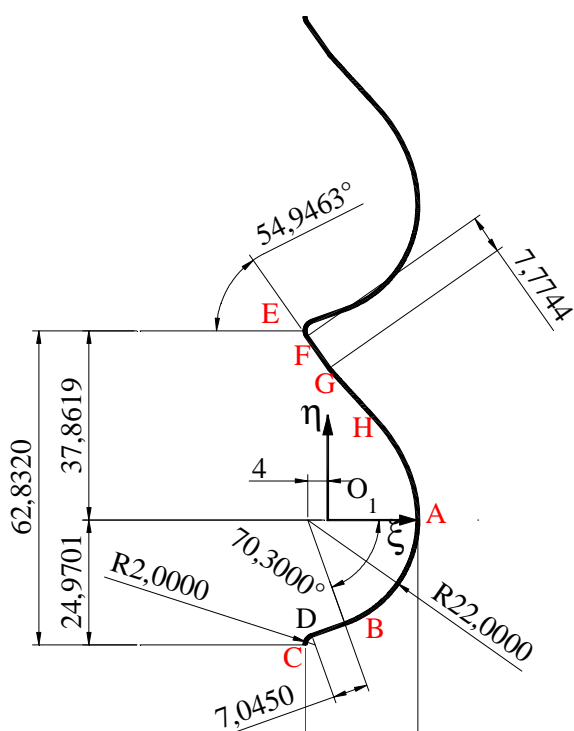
Forma constructivă a cremalierii, varianta IV
